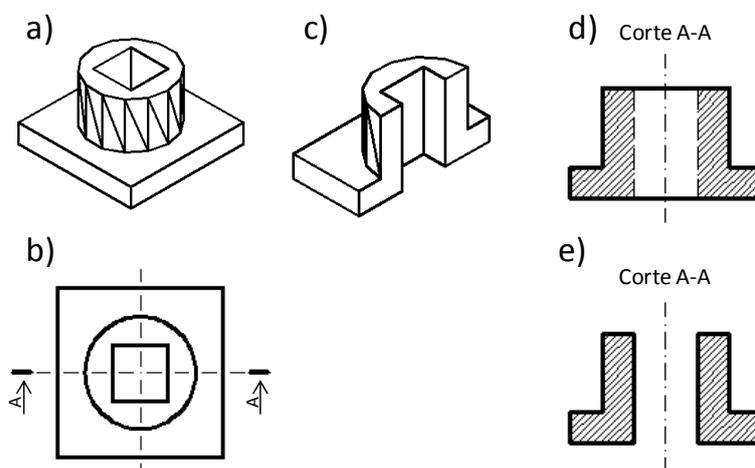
Objeto a 3D (a), planta com indicação do plano de corte (b), objeto cortado (c), vista cortada (d) e secção (e).
